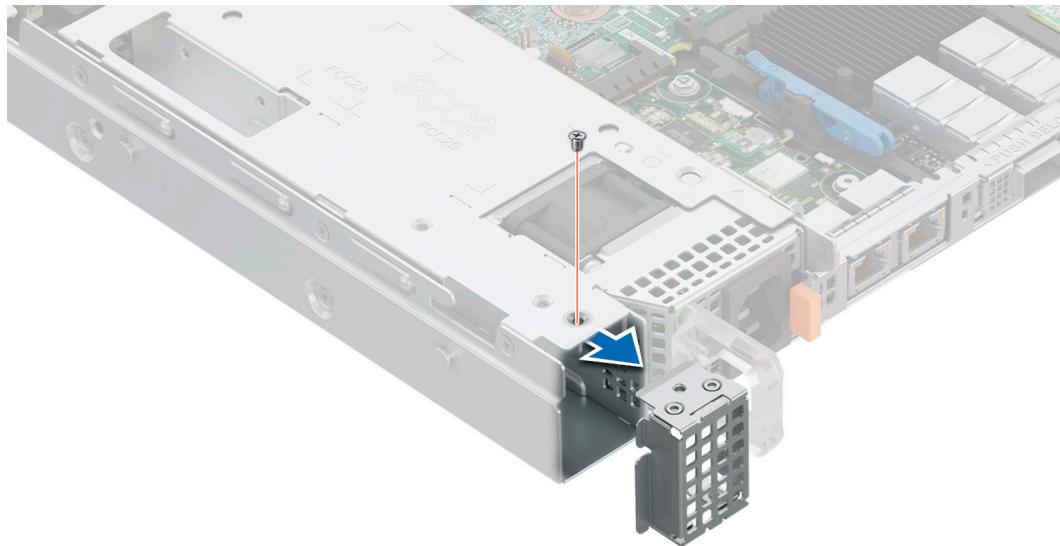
Entfernen des BOSS-N1-Modulplatzhalters
